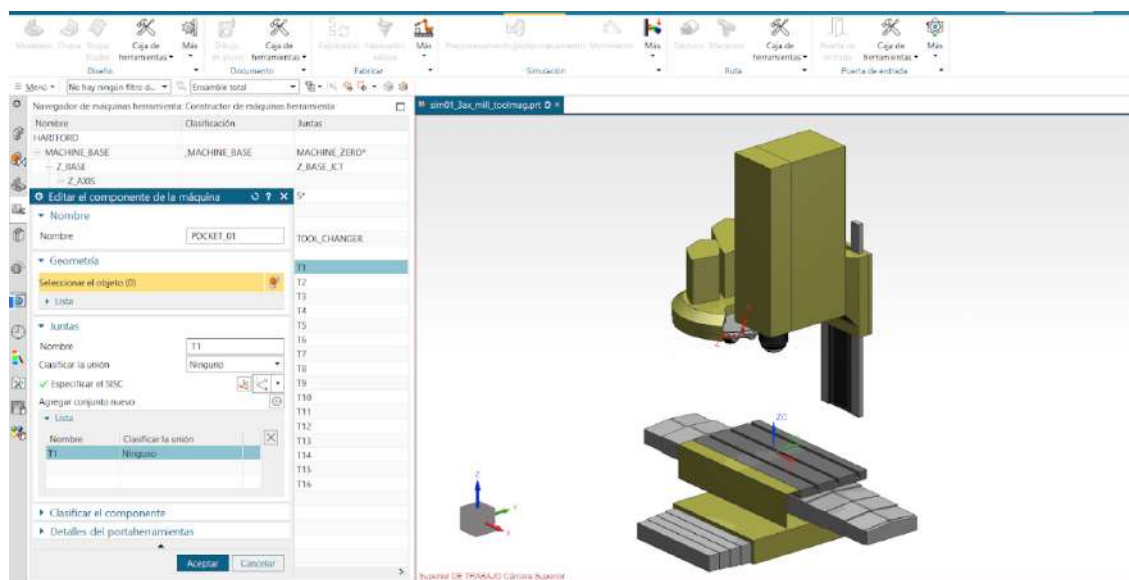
Definición del *Pocket 1* del Cambiador Automático de Herramientas.
